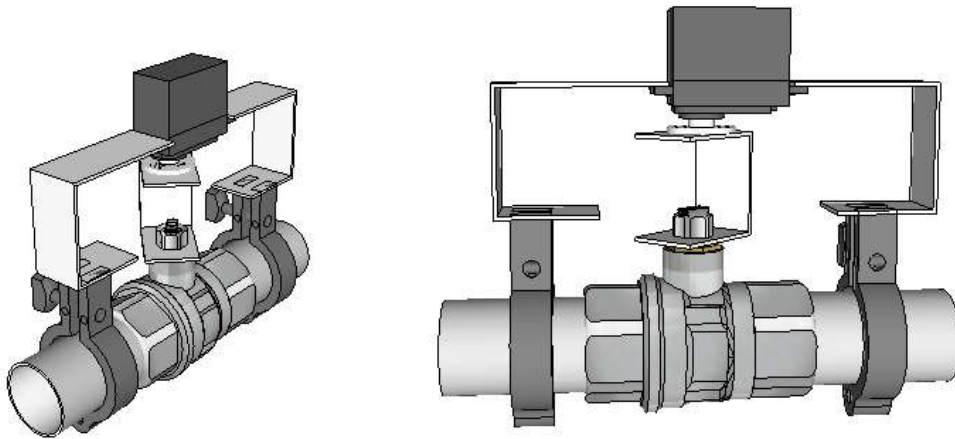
Dibujo en 3D de primer diseño de la válvula.
